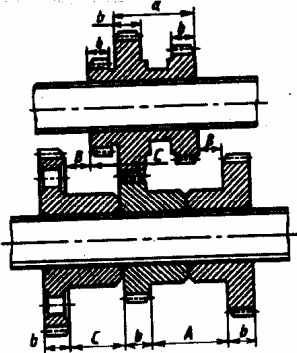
(а). Схема расположения зубчатых колес в коробках передач для двухступенчатых коробок
